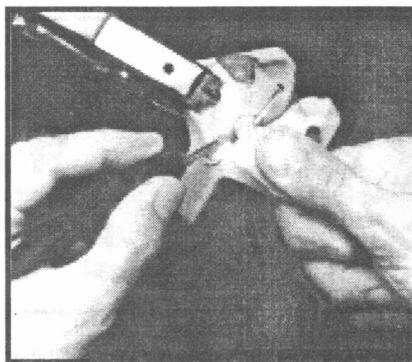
Пресс-формы из готовых резиновых шипов
